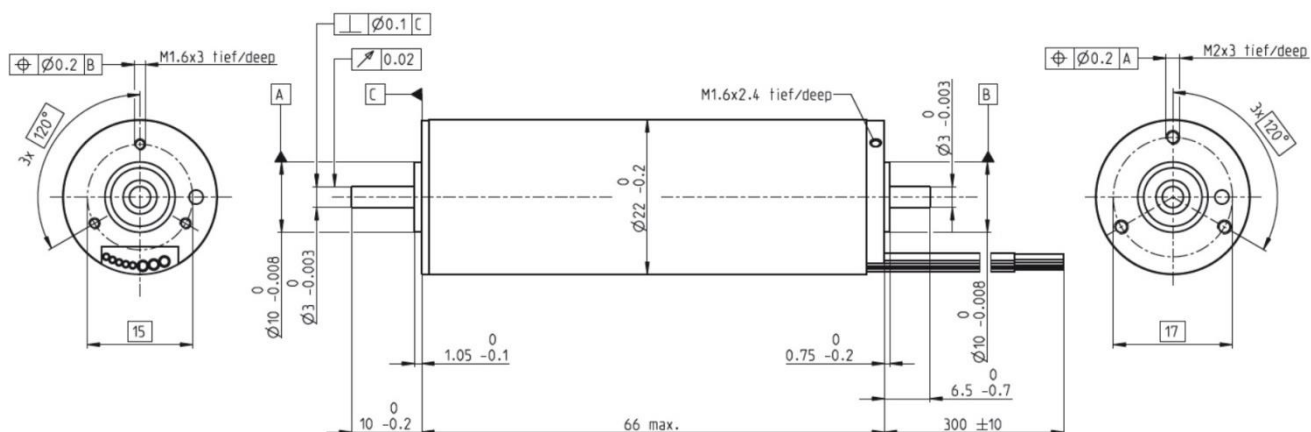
Dimensões do motor de tração Maxon EC4Pole 22
